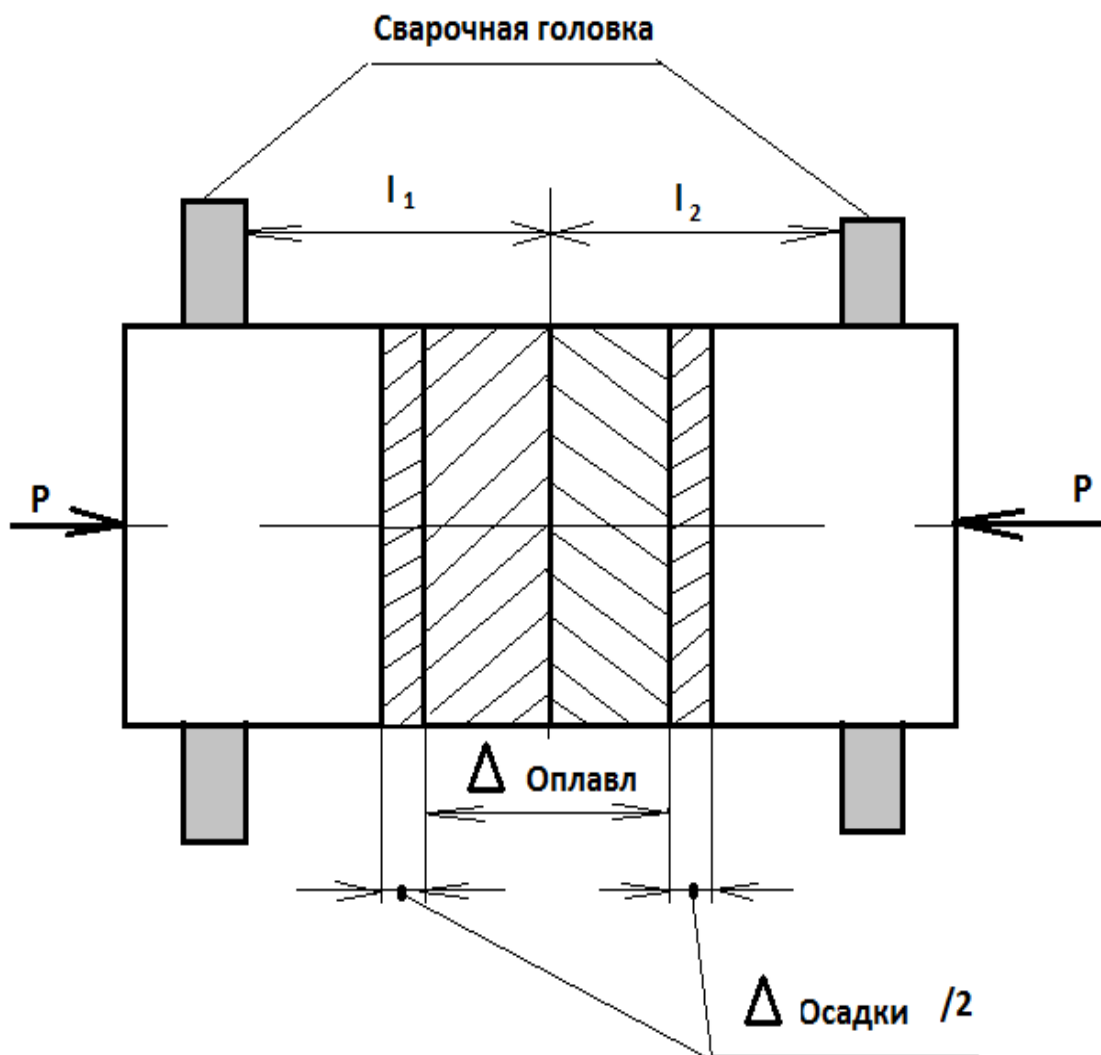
Установочные параметры сварного шва при стыковой сварке оплавлением.
